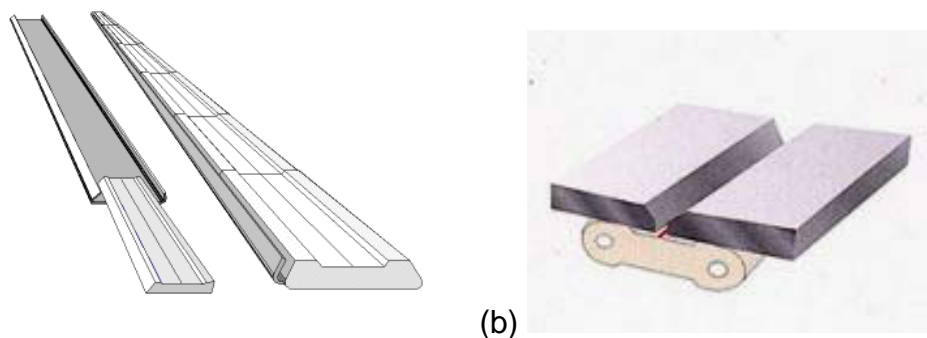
Fixação esquemática do suporte cerâmico com fita adesiva de alumínio (Obsidian Welding Backing, 2013).
